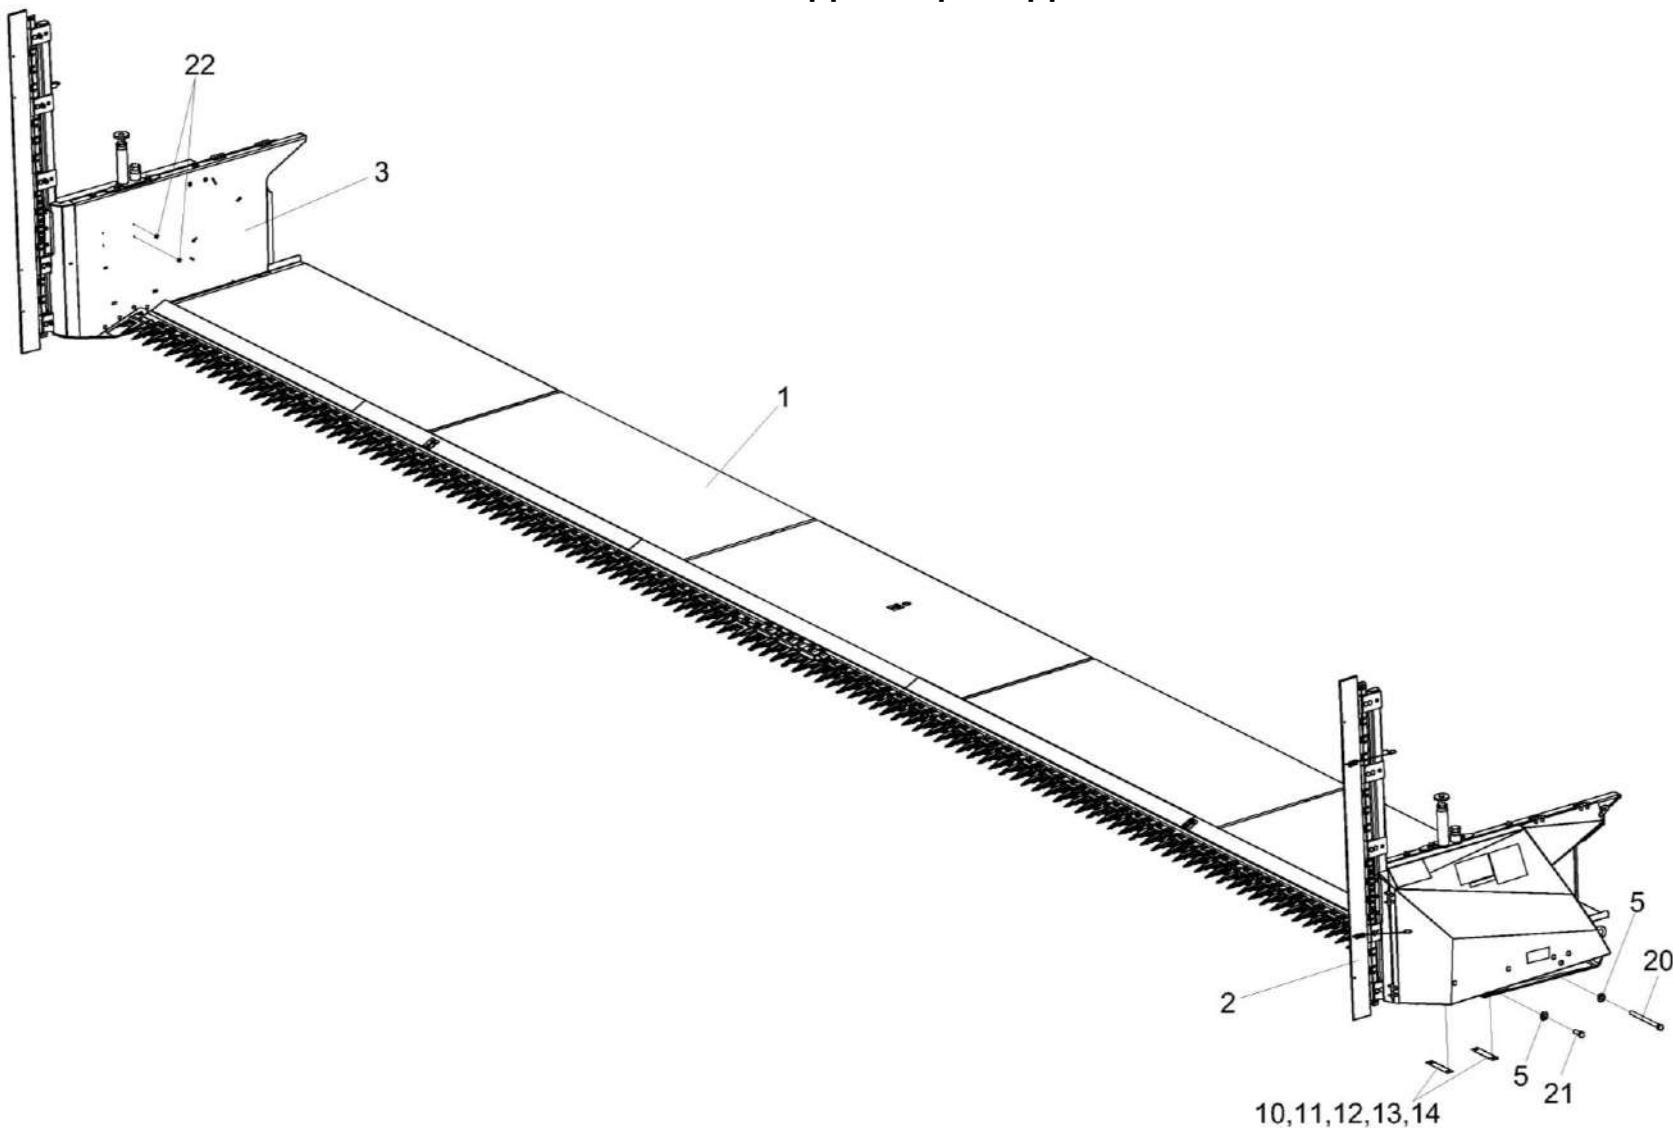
Приспособление для уборки рапса ПР-9 КЗК-9-2540000
